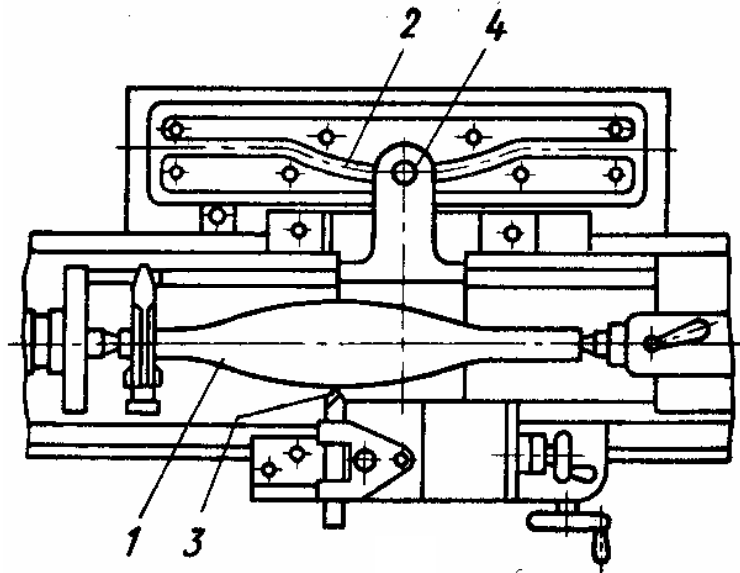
Схема обробки фасонної поверхні заготовки за копиром: 1 – заготовка; 2 - копір; 3 - різець; 4 - шуп
